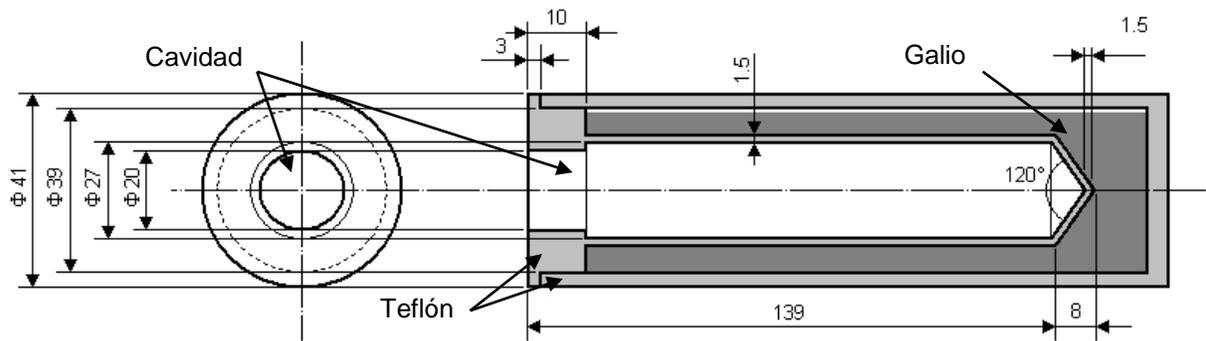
Dimensiones del nuevo diseño de cuerpo negro.
